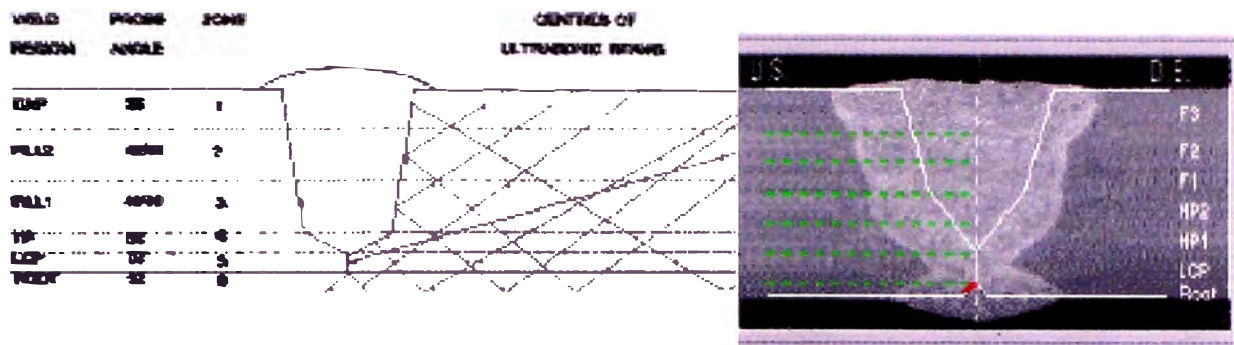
Mapeo del Cordón de Soldadura
